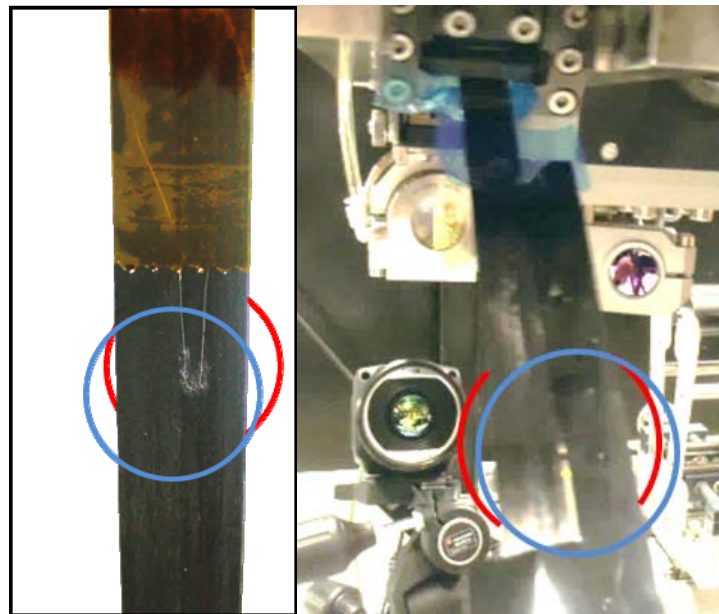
Thermocouples soudés sur chaque face du tape (gauche) ; configuration du montage expérimental (droite)
